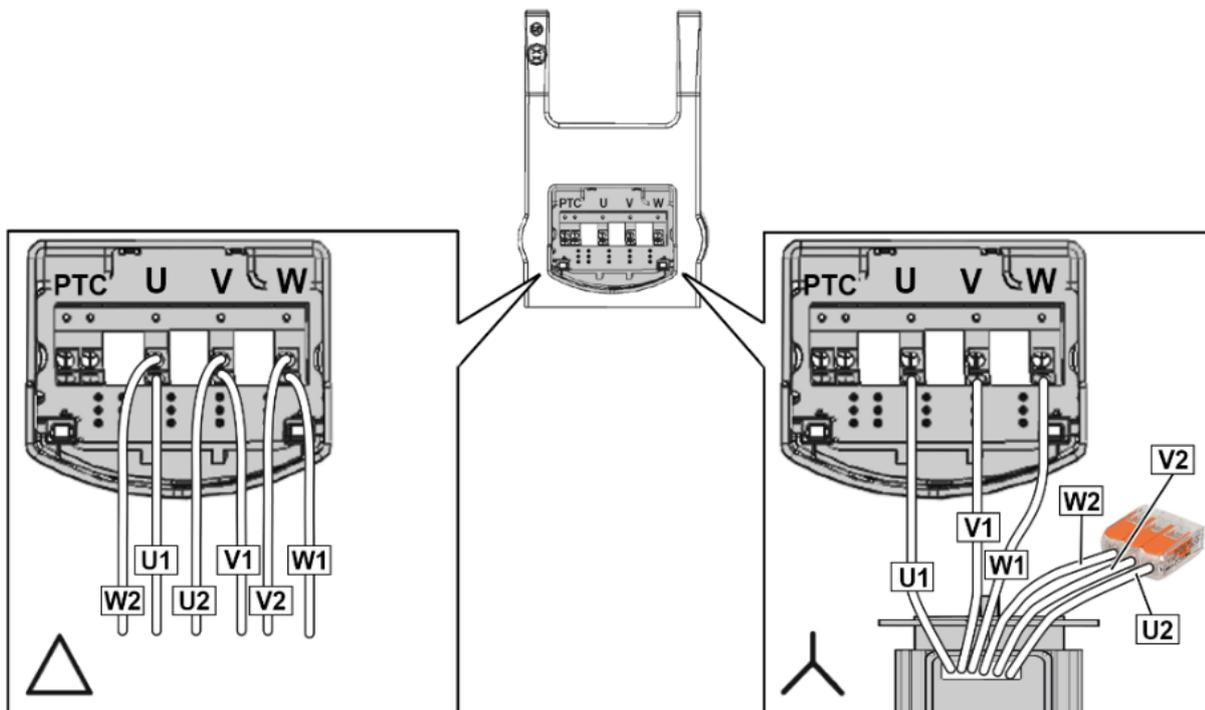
Stern- oder Dreieck-Schaltung BG A
